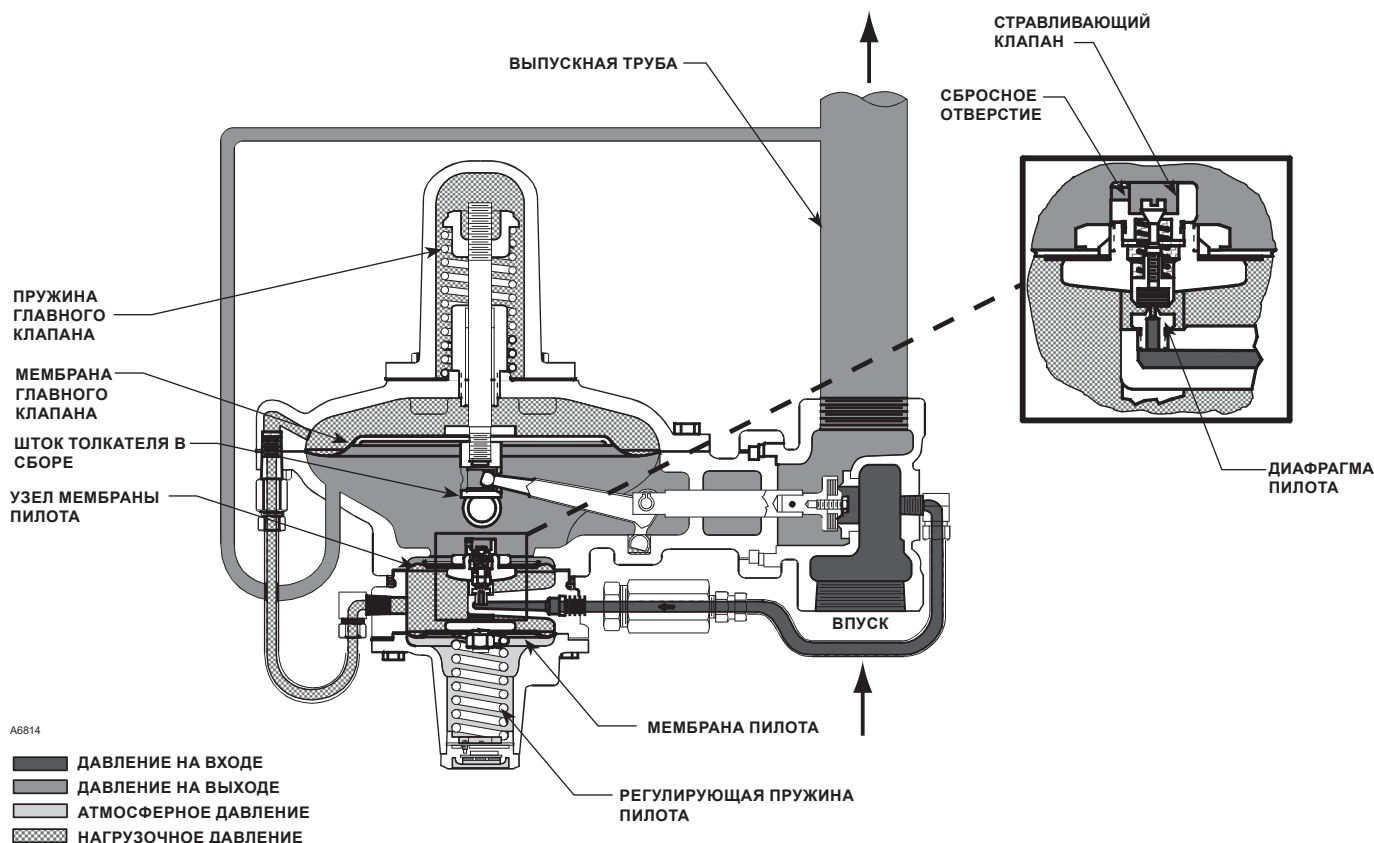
Схема регулятора типа 99 с пилотом типа 61L (низкое давление)
